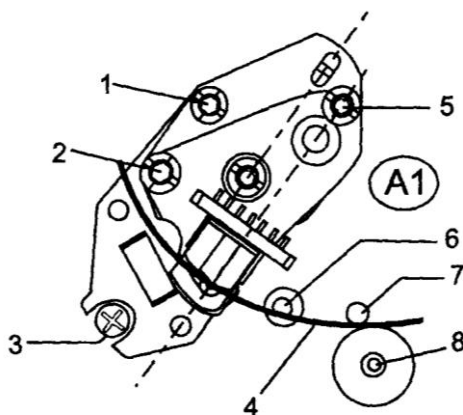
Регулювання положення комбінованої головки : 1 — гвинт установки висоти; 2 — гвинт установки азимута; 3 — ексцентриковий Х-подібний гвинт; 4 — стрічка; 5 — гвинт установки кута нахилу; 6 — механізм, що направляє стрічку; 7 — ведучий вал; 8 — притискний валик
